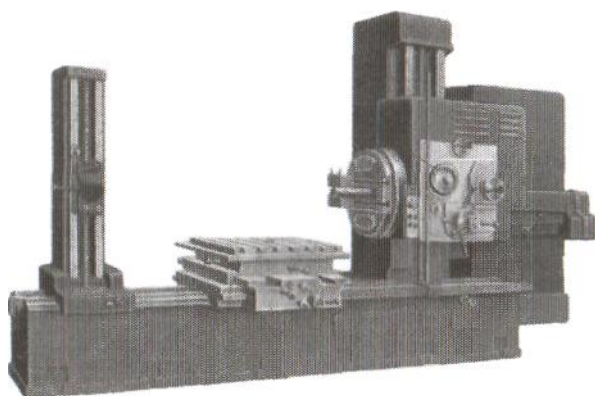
Общий вид горизонтально-расточного станка модели 262Г
